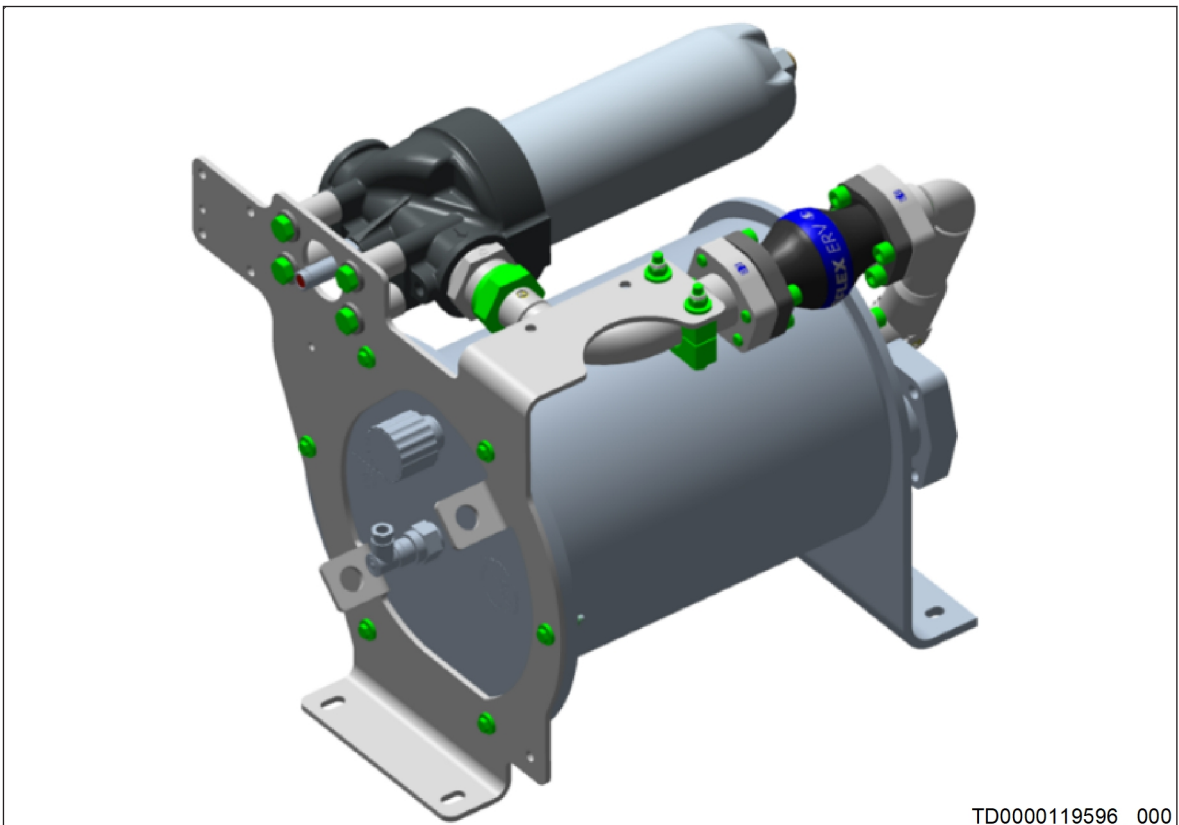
Hydrauliköl Ausgleichsbehälter mit Sachnummer X50441300480/87
